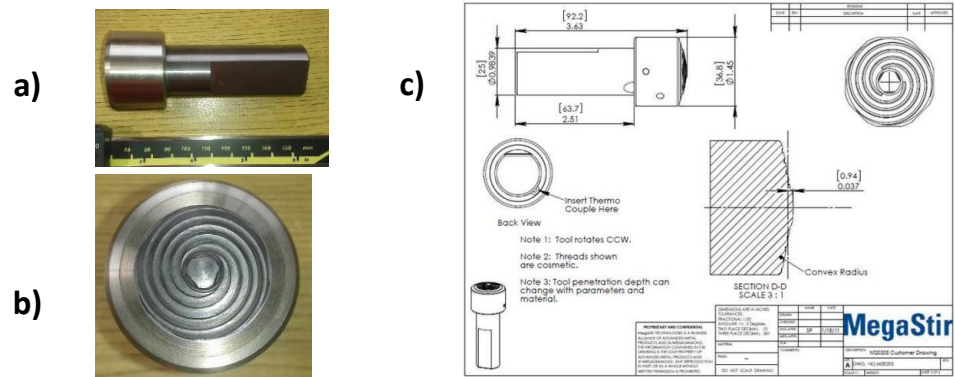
Esquema de herramienta para unir soldadura FSSW en espesor de lámina 1.5 mm. a) vista lateral de la herramienta, b) vista frontal de la herramienta y c) plano de la herramienta
